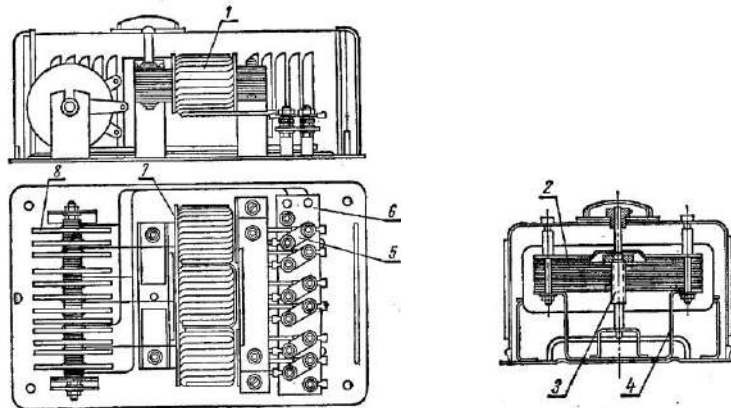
Компаундирующее устройство типа УКУ-3М: 1-катушка; 2-подвижное ядро магнитопровода; 3- регулировочный винт; 4-скоба; 5-перемычки; 6-щиток зажимов; 7- трехфазный трансформатор тока; 8-селеновый выпрямитель
